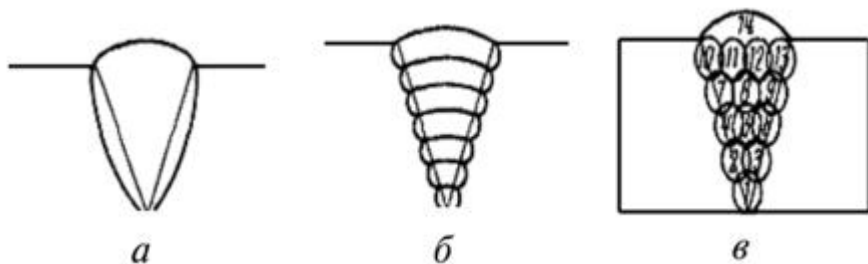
Схемы сварных швов: а — однопроходный; б — многослойный; в — многопроходный
